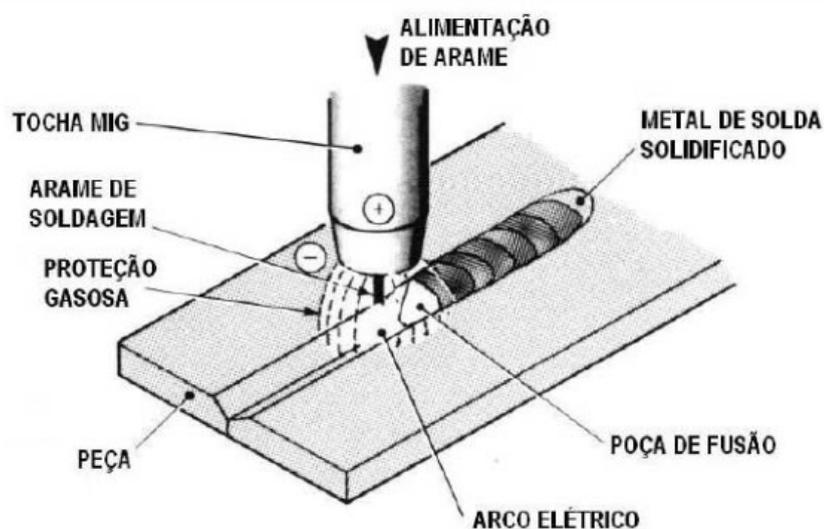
Processo de solda MIG/MAG. (Processo de Soldagem MIG MAG, 2021)
